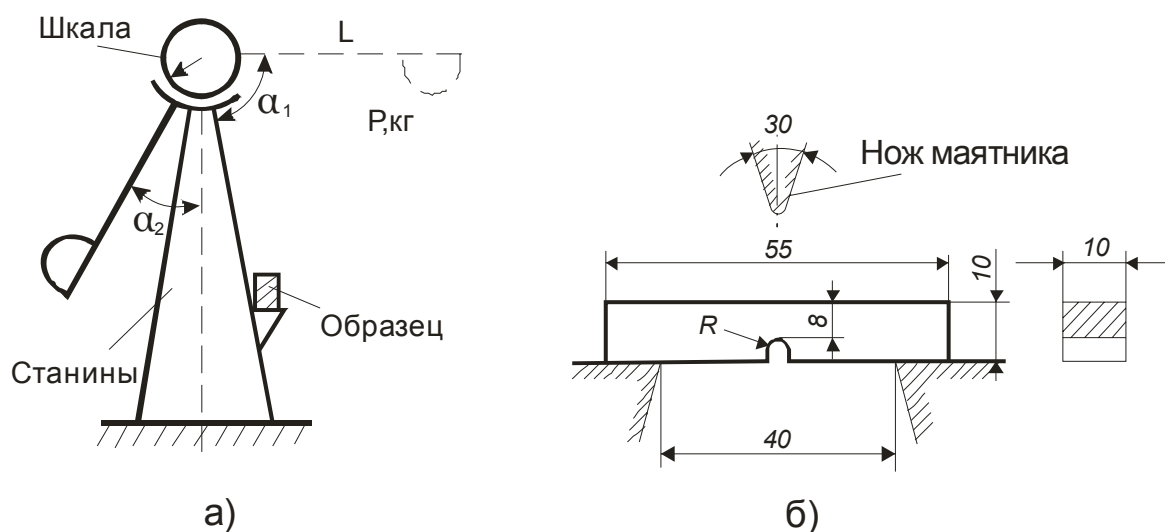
Схема маятникового копра (а) и образец (б) для испытаний на ударную вязкость
